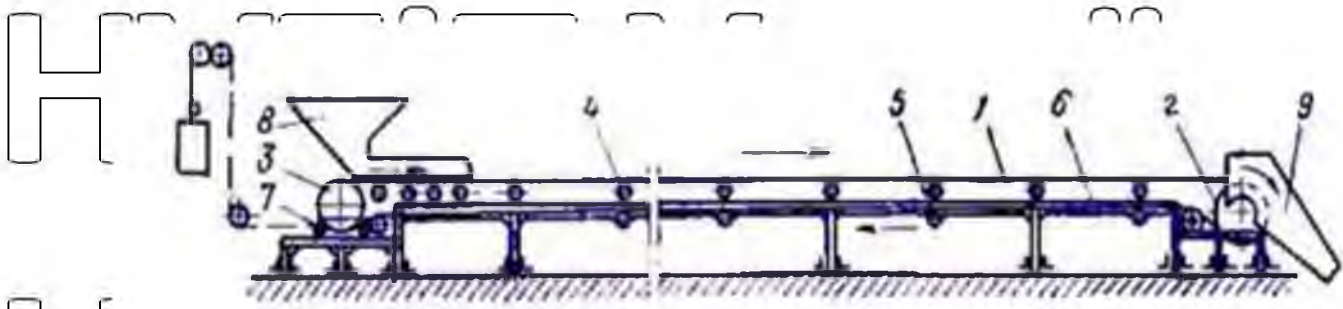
Схема стрічкового конвеєра: 1 – стрічка; 2 – приводний барабан; 3 – натяжний барабан; 4 – роликові опори; 5 – роликові опори порожньої гілки; 6 – опорна рама; 7 – натяжний пристрій; 8 – завантажувальна воронка; 9 – розвантажувальний жолоб
